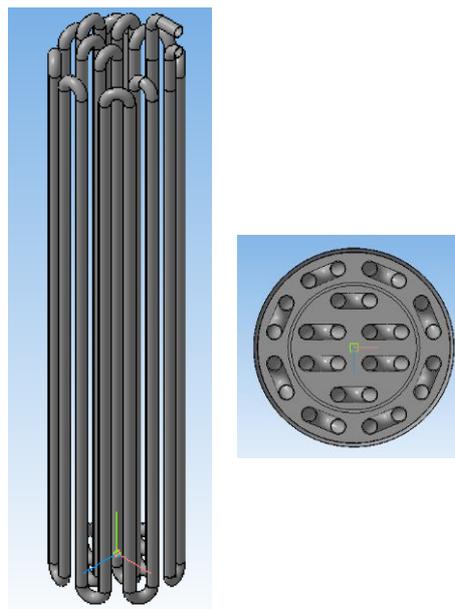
Трубный змеевик и поперечный разрез цилиндрической печи
